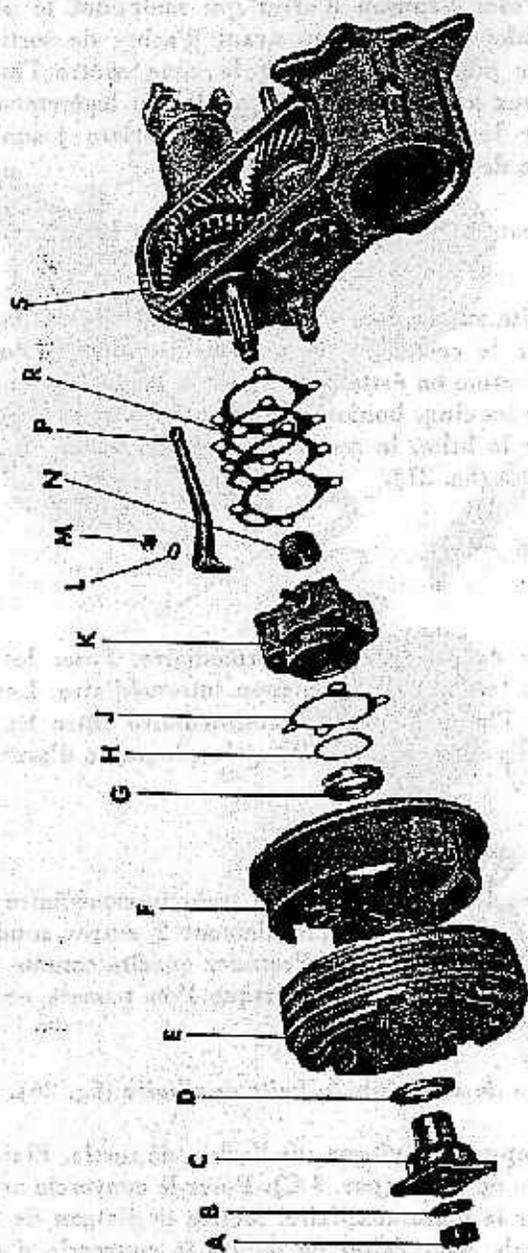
Couvrerie d'arbre de sortie. Vue éclatée.
